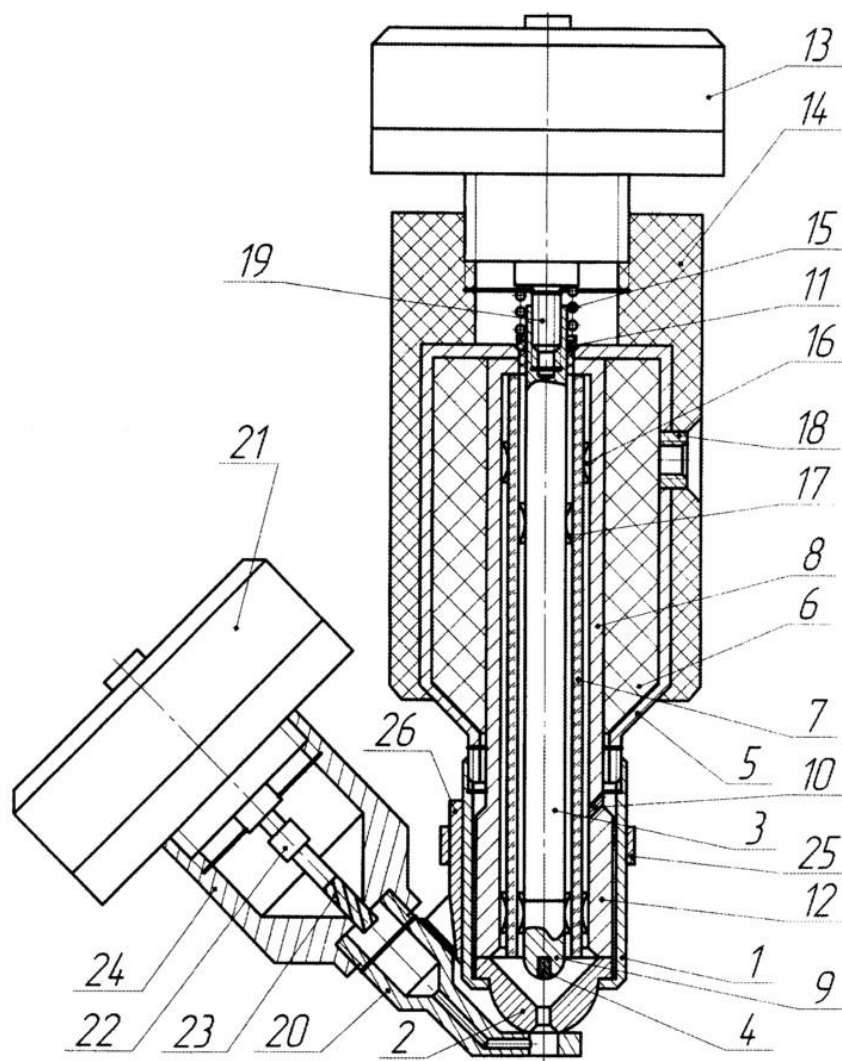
Портативный плазмотрон для напыления и наплавки покрытий [11]
